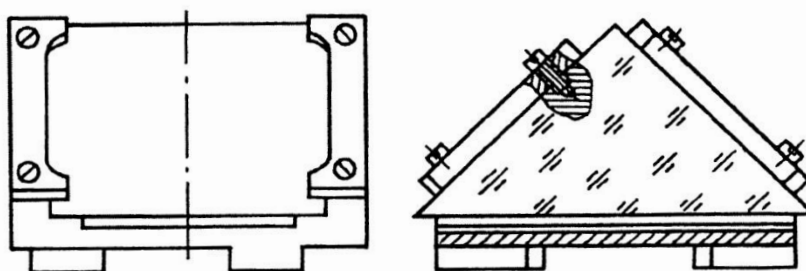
Кріплення призми БР-180° прижимними планками
